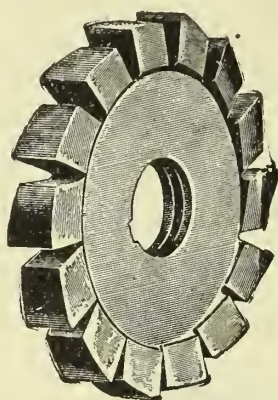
Hinterdrehter Scheibenfräser, an 3 Flächenschneidend.
